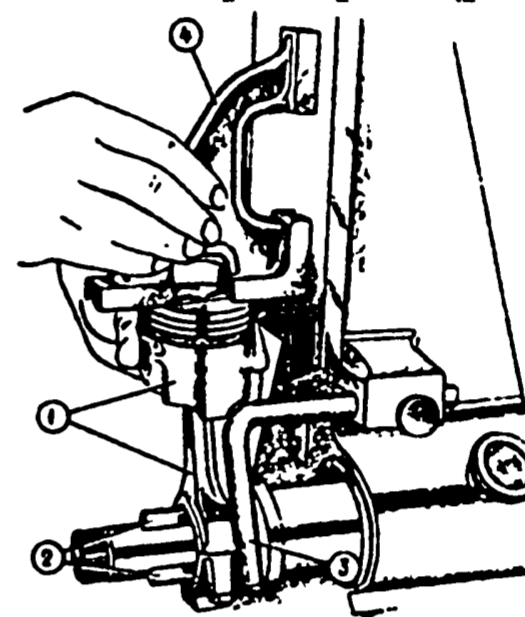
Проверка параллельности осей поршня и шатуна: 1 - собранный комплект шатун - палец - поршень; 2 - выдвижные ножи; 3 - упор; 4 - калибр
